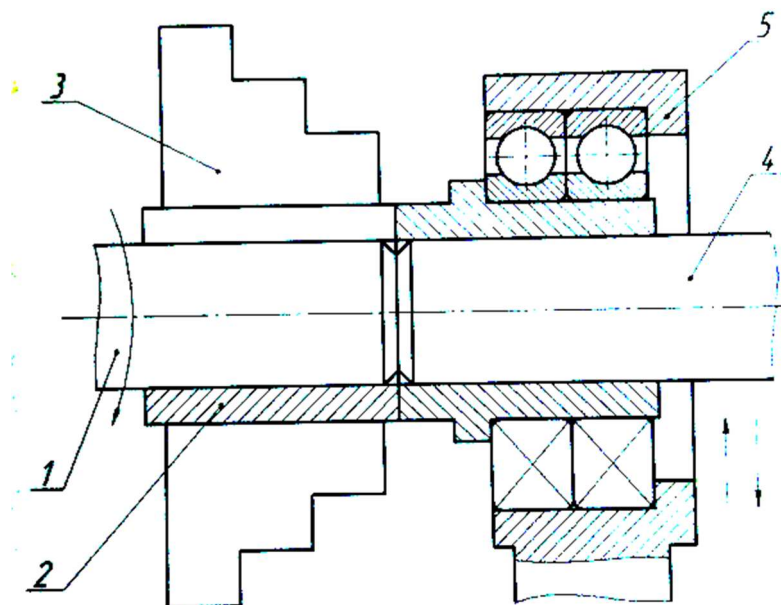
Схема устройства для разделения прутка на мерные заготовки в токарном станке:
